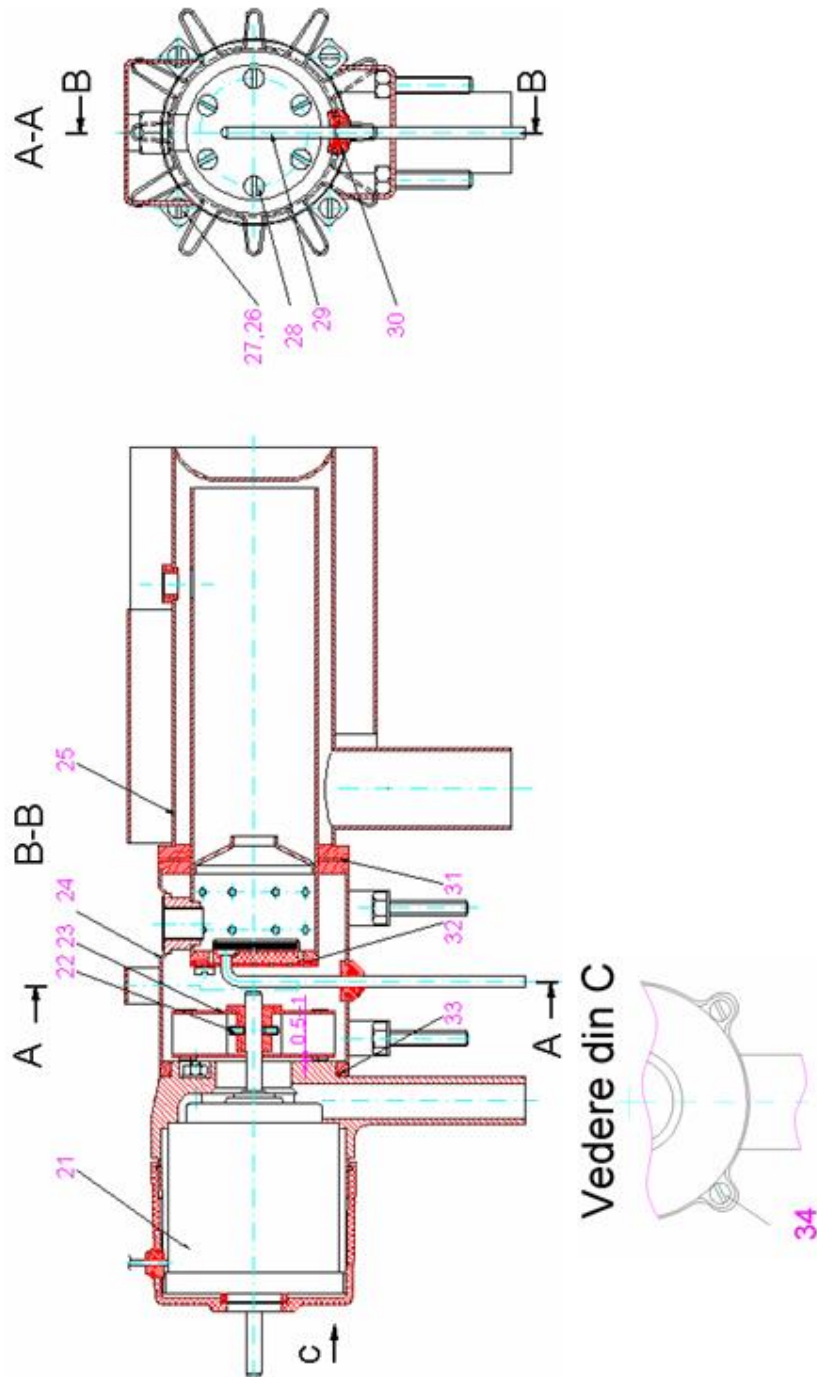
a Subansamblul grup motor, arzător, schimbător de căldură
